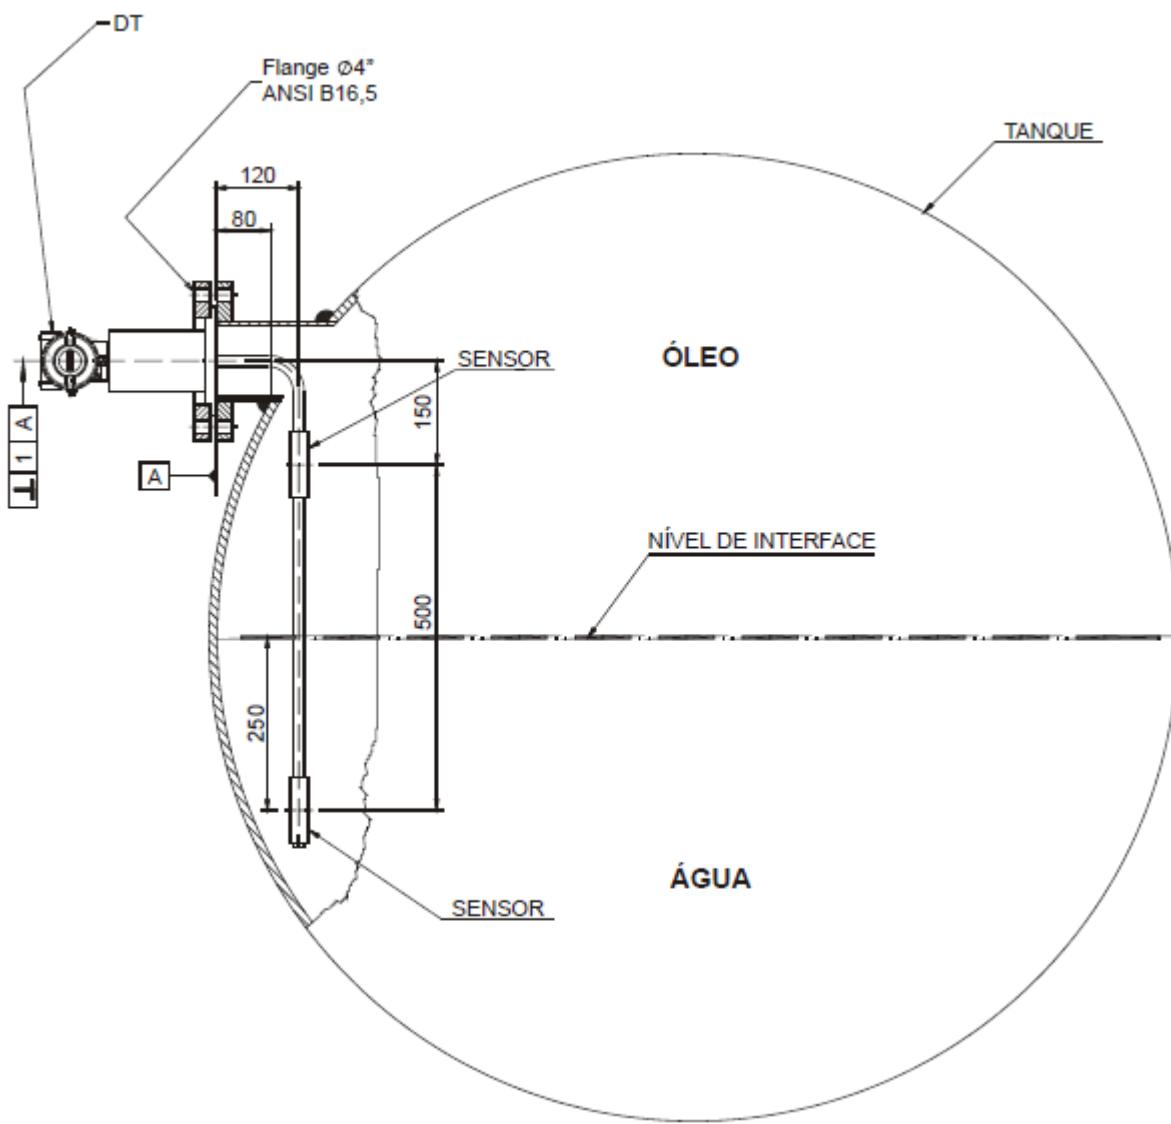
Tipos de Instalação para o DT302 (M)
